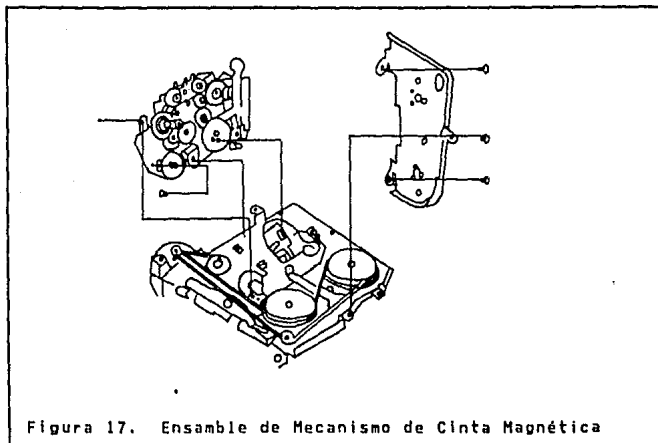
Ensamble de Mecanismo de Cinta Magnética
